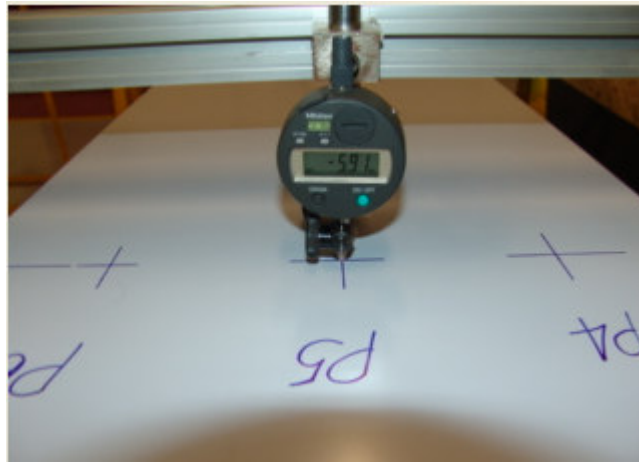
Fotografia da medição da planeza do ponto P5 no conj. painel colado.
